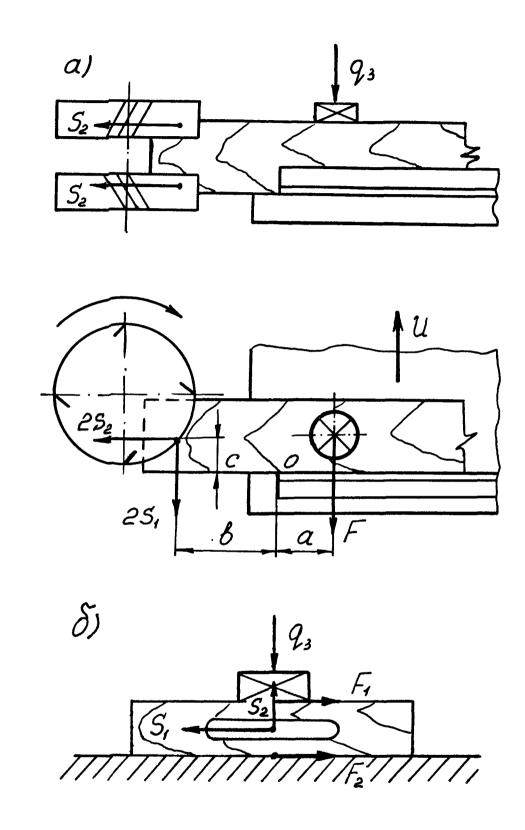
Расчетные схемы для определения давления зажимного устройства: а - станок с подачей заготовки кареткой; б - станок с подачей заготовки столом
